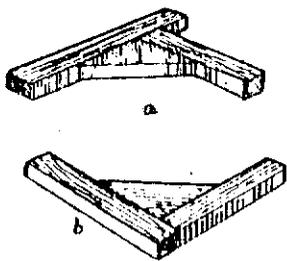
Cales d'encoignures a) mauvais, b) bon.
